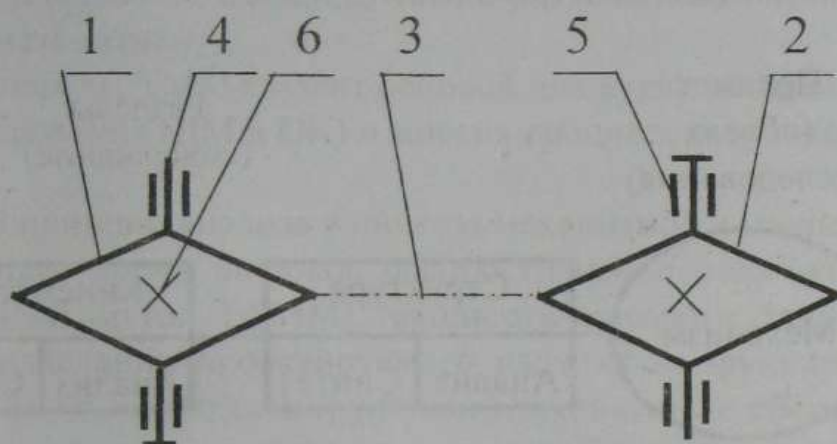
Схема передаточного механизма – цепной передачи:
